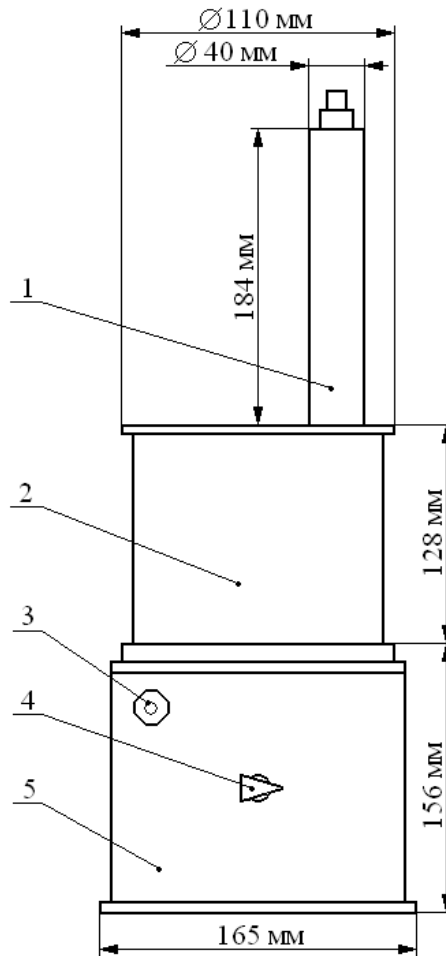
Высоковольтный делитель напряжения: 1 – активное сопротивление; 2 – конденсатор; 3 – соединительный разъем; 4 – переключатель; 5 – корпус.
